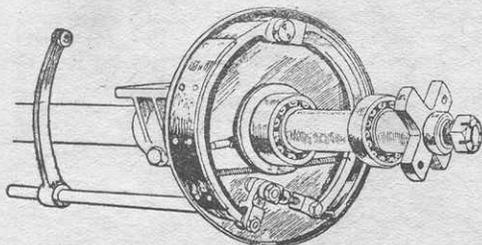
Тормоз с внутренними колодками заднего колеса автомобиля с карданной передачей.
